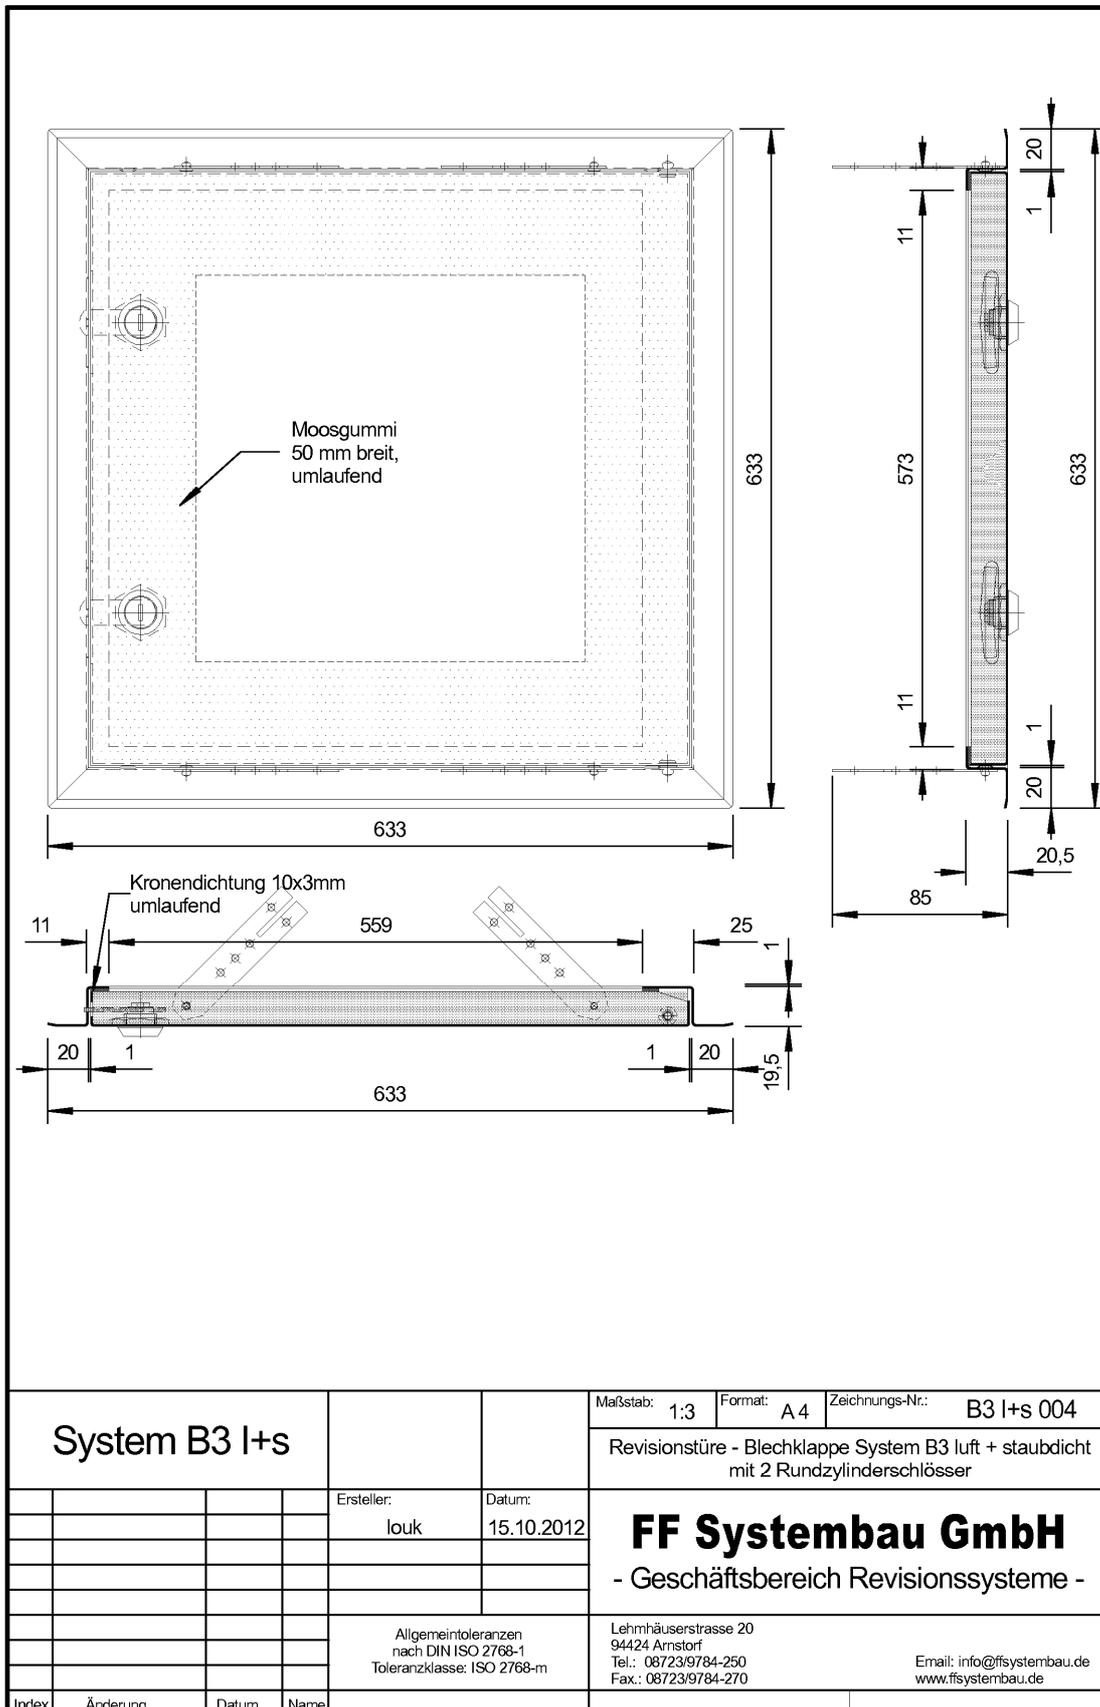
Zeichnung zu Probekörper 2, Rundzylinderschlösser
